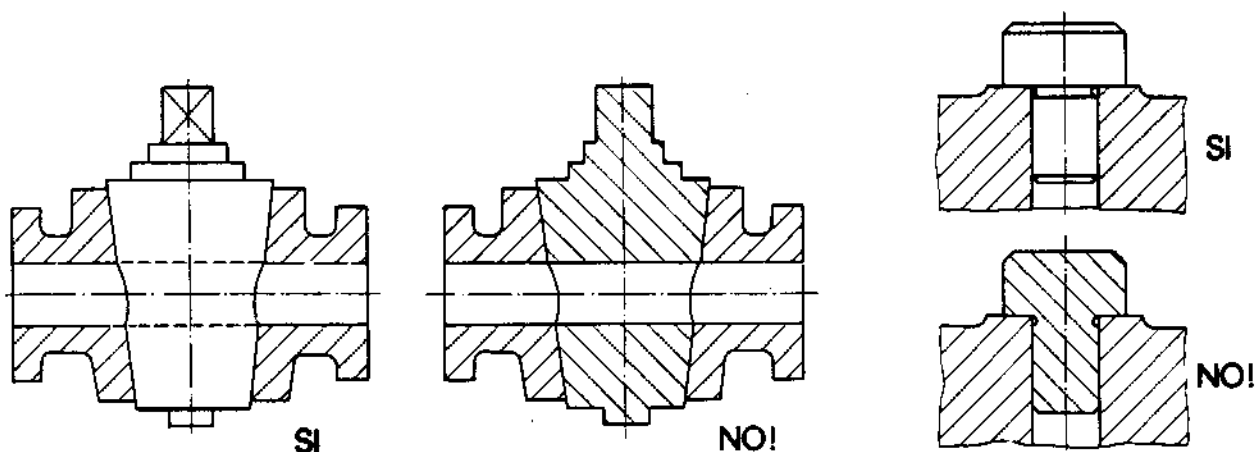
I maschi dei rubinetti non si sezionano quando il piano di sezione è longitudinale.
